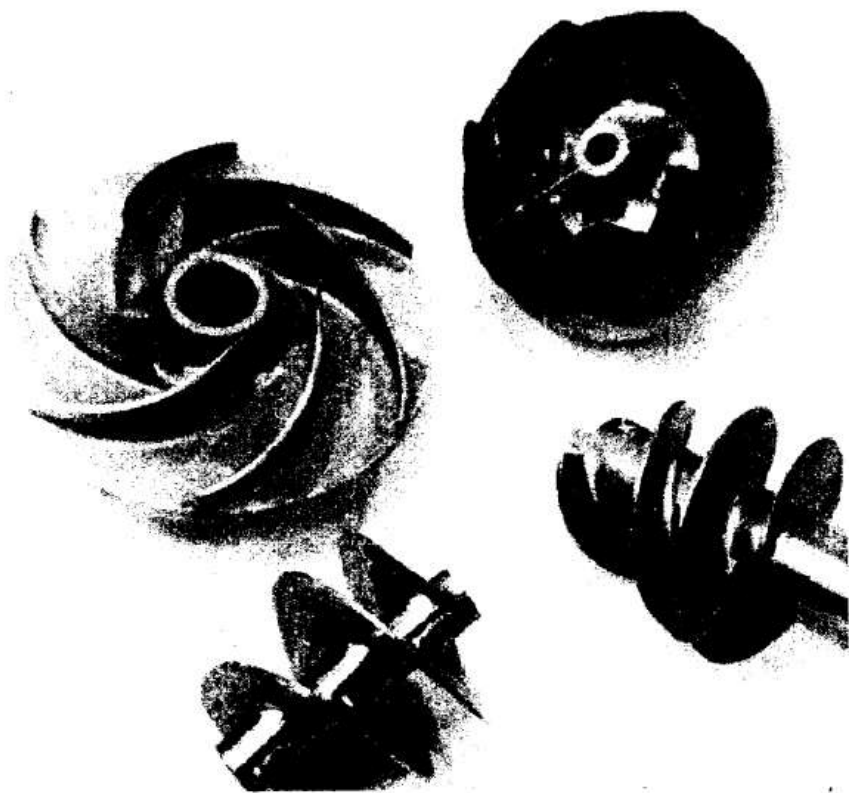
Типовые детали турбонасосных агрегатов с открытыми поверхностями сложного профиля
